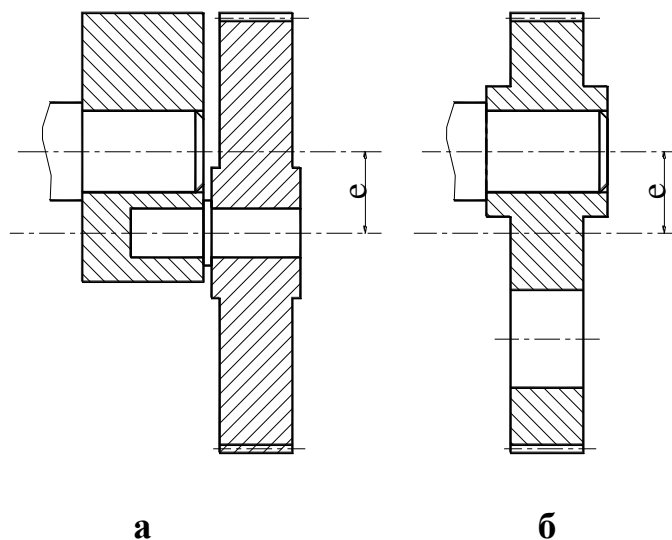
Варіанти конструкції центрального колеса:
